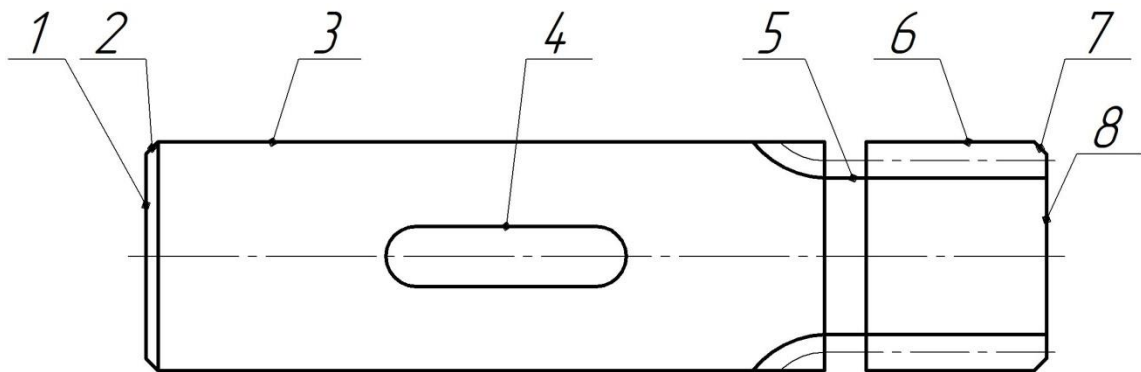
Ескіз деталі з номерами поверхонь
